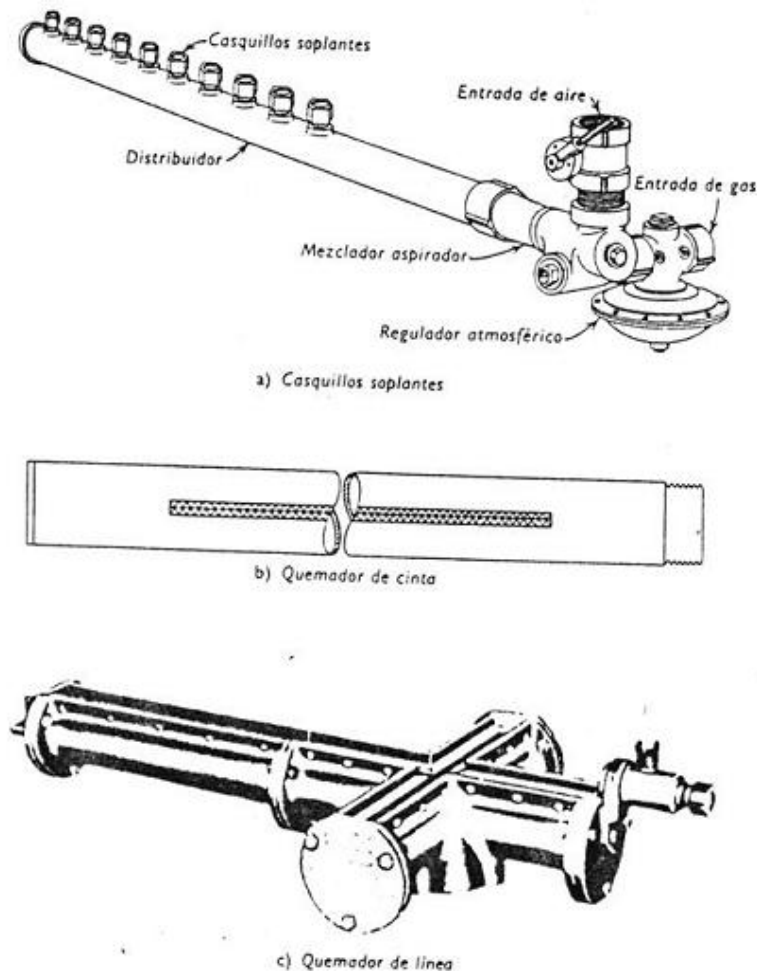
Quemadores de casquillos, cinta y línea
